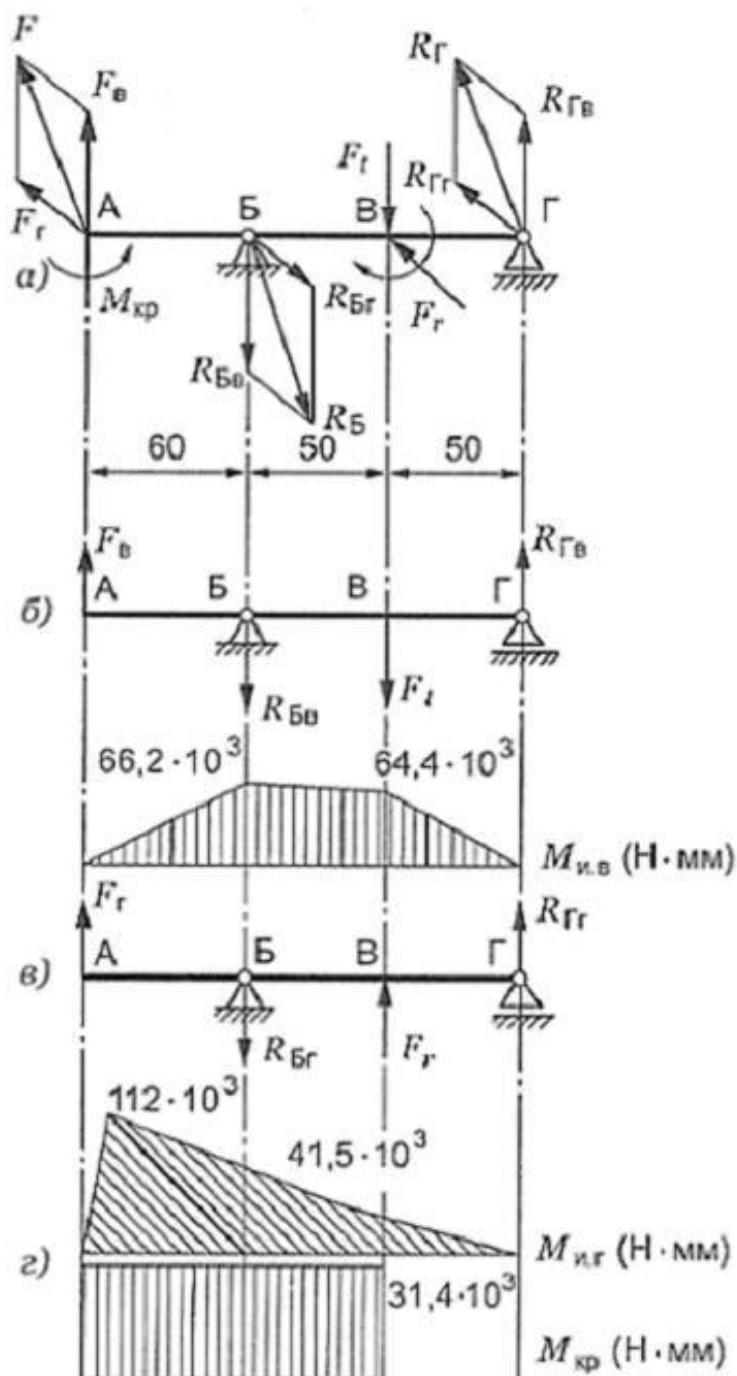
Расчетная схема тихоходного вала редуктора.
